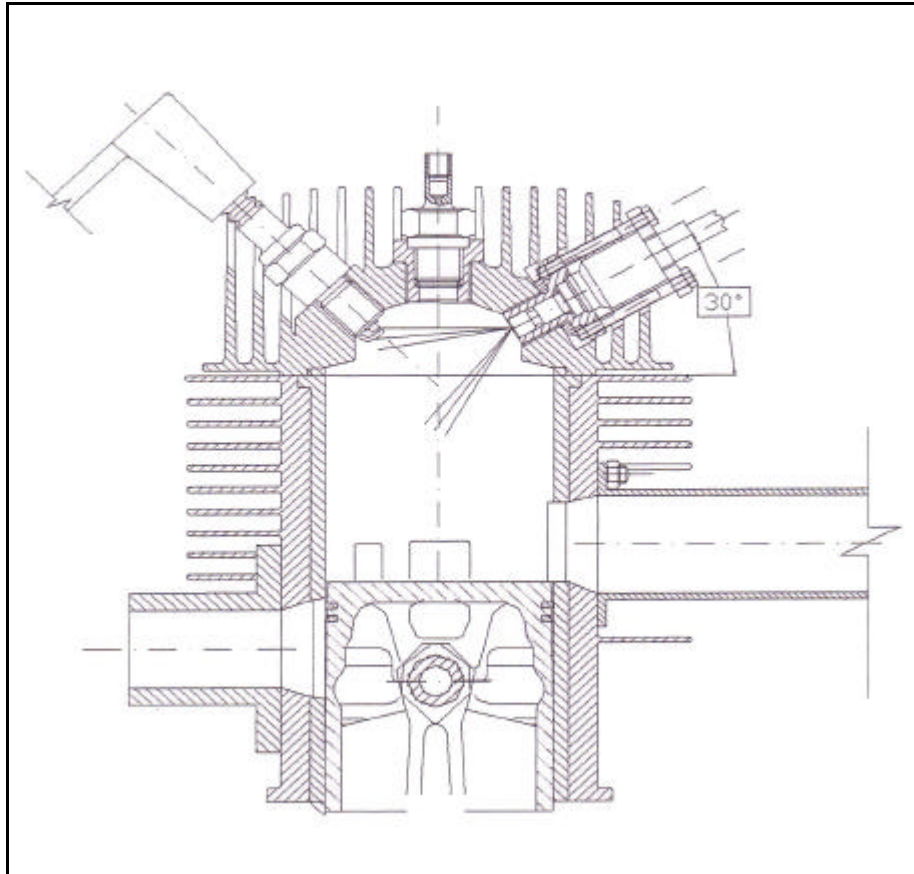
Sezione Benelli 1FB 1226 in configurazione ad iniezione diretta
